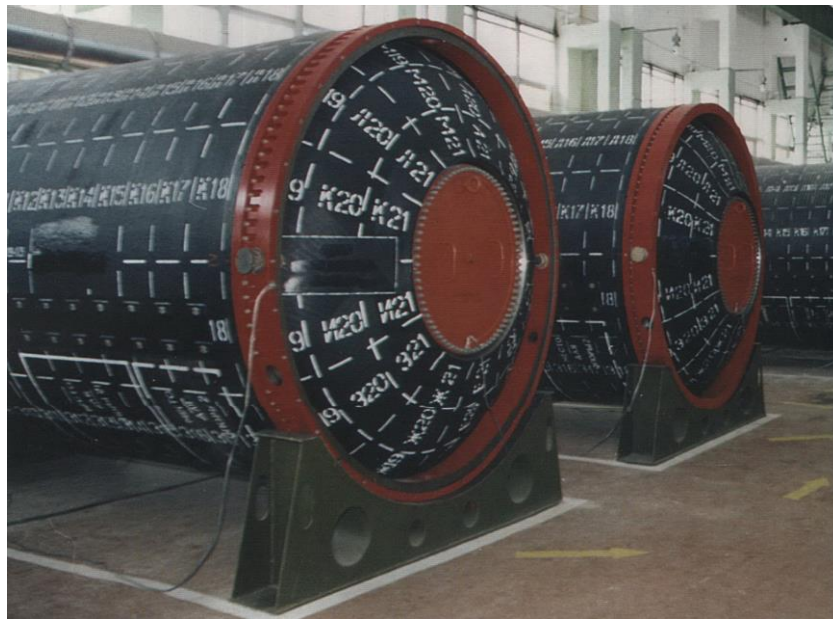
Споряджений корпус твердопаливного ракетного двигуна першої ступені РС-22
